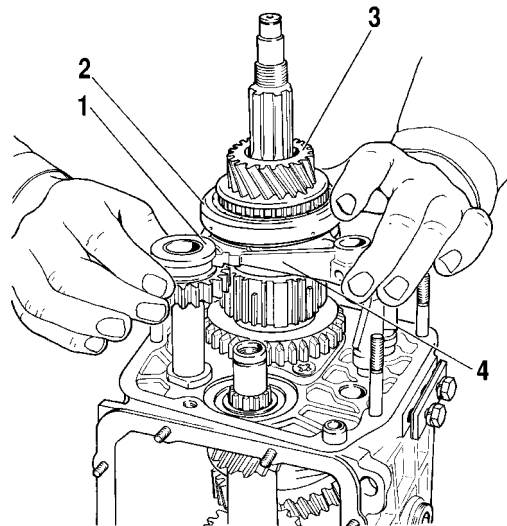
Отвертывание болтов крепления блока шестерен и вилки включения V передачи и заднего хода:
